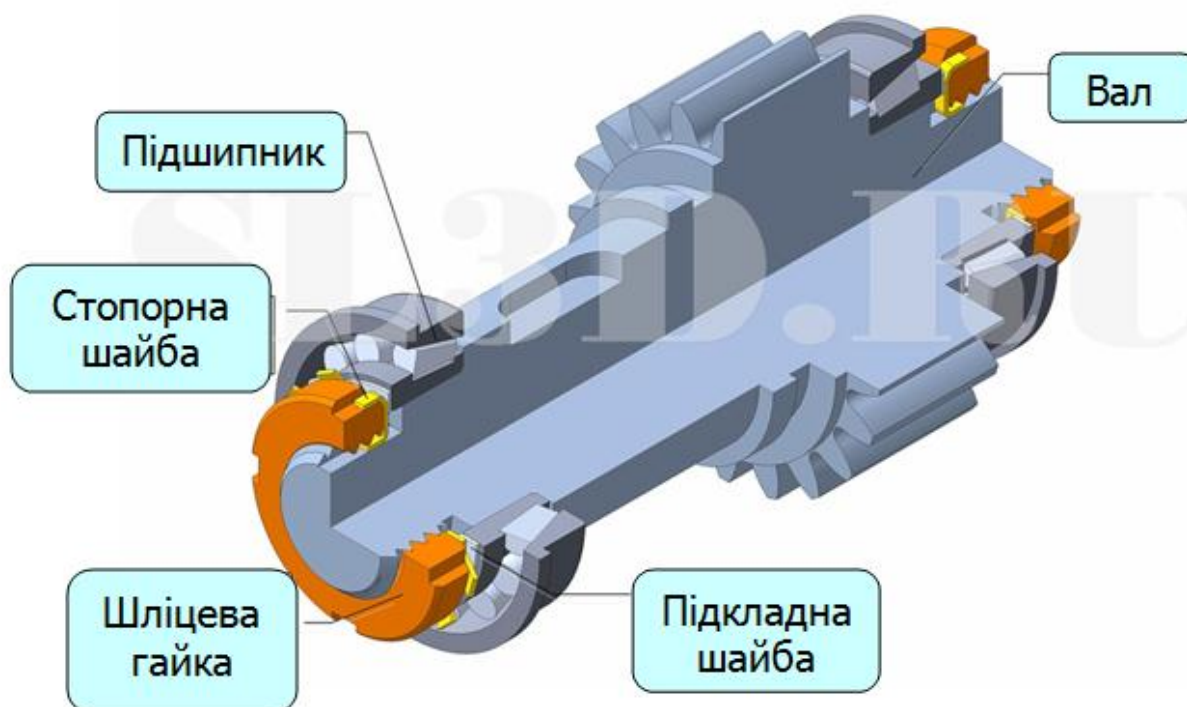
Установка підшипника за допомогою шліцевої гайки і підкладної шайби
